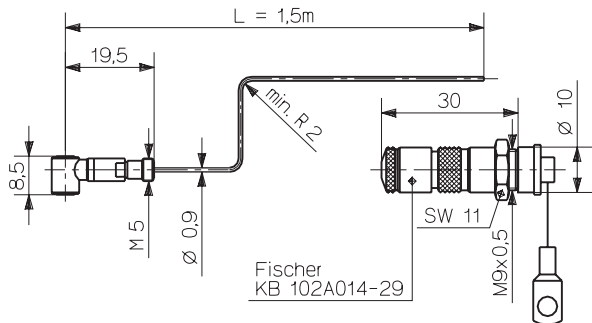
Kraftsensor Typ 9213BE mit Kabel und Stecker
